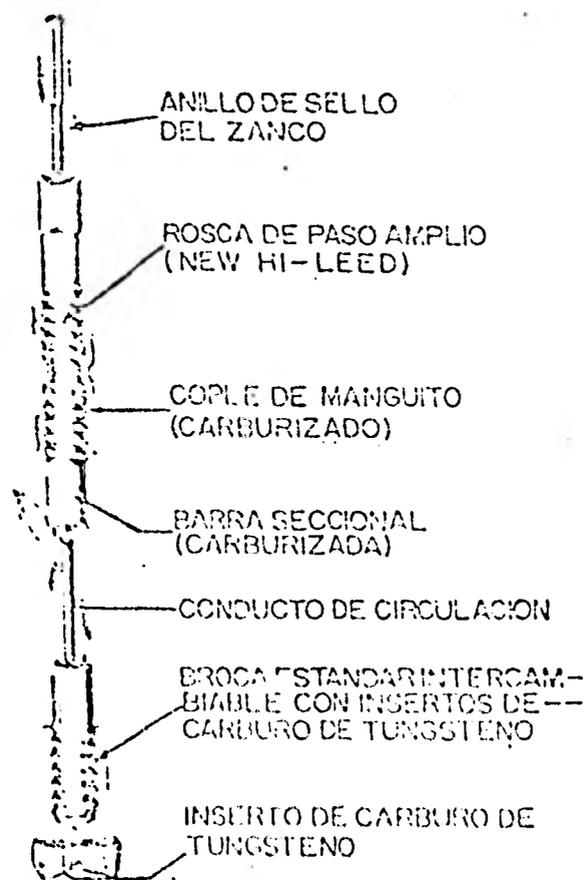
ESQUEMA DEL ACERO SECCIONAL DE BARRENACION
